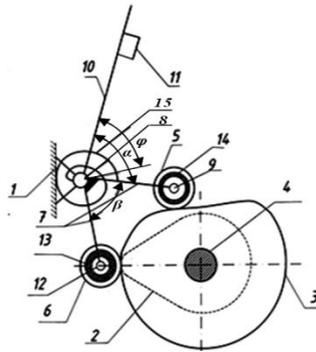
Батанный механизм ткацкого станка с составными роликами кулачка
